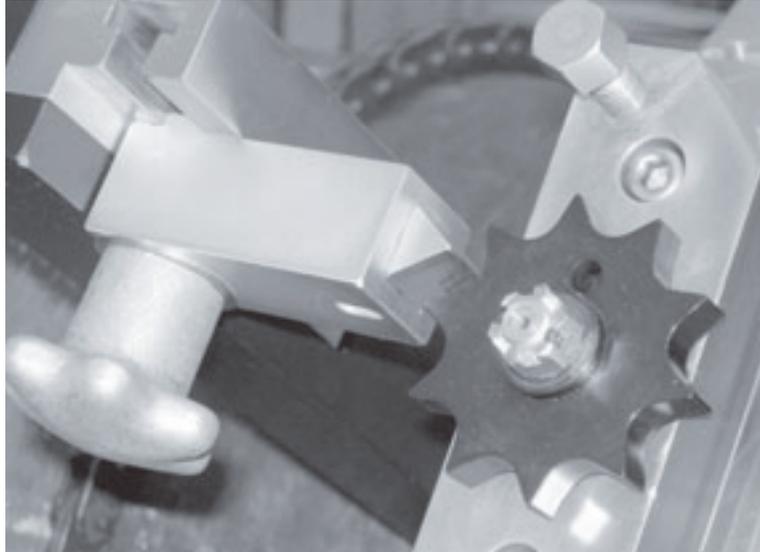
Ziehen Sie die Federspannschrauben vollständig zurück, um die Werkzeugschlitten federzubelasten.
